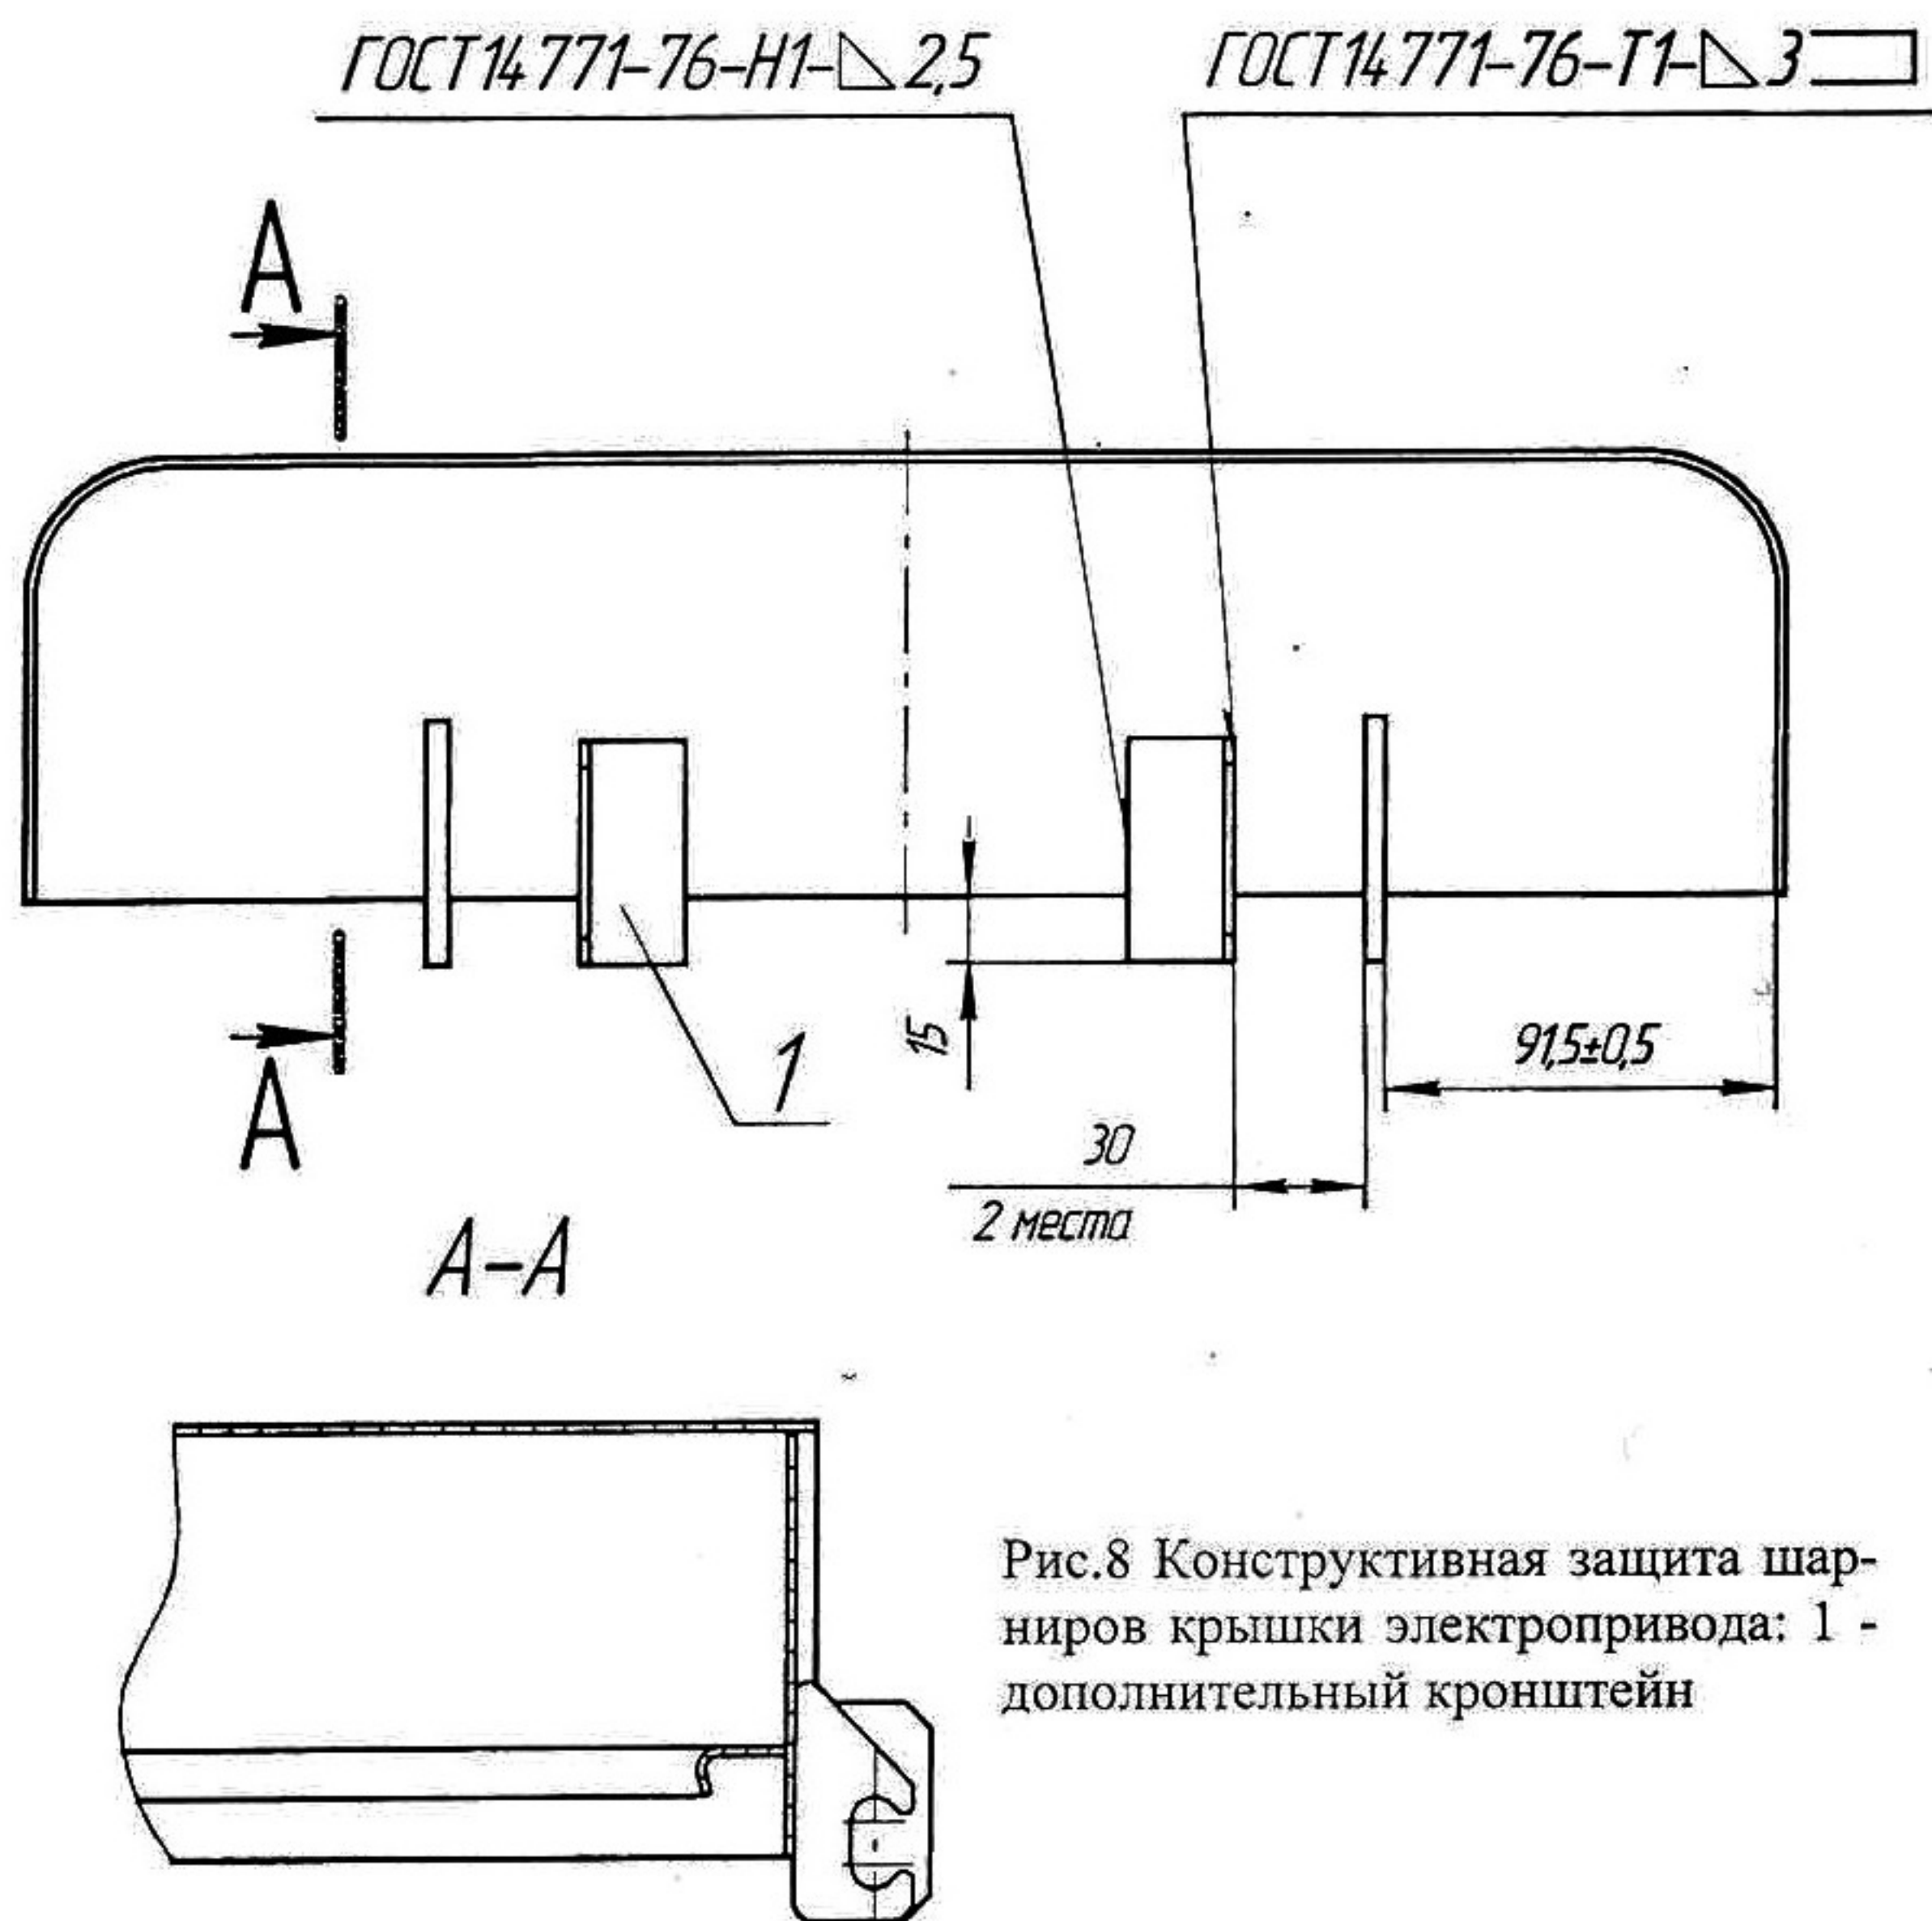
Конструктивная защита шарниров крышки электропривода: 1 - дополнительный кронштейн
